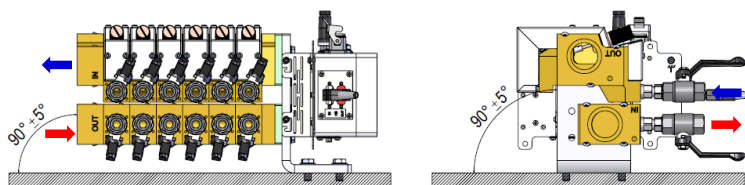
Posizione di montaggio orizzontale esecuzione a destra
